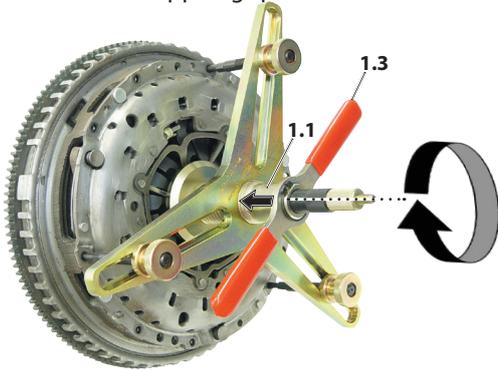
Befestigungs-Schrauben eindrehen und nachfolgend SAC-Kupplung entspannen.
